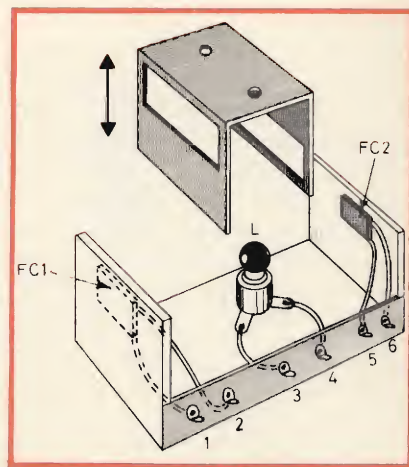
Disegno illustrante la struttura interna della parte meccanica del pedale.
